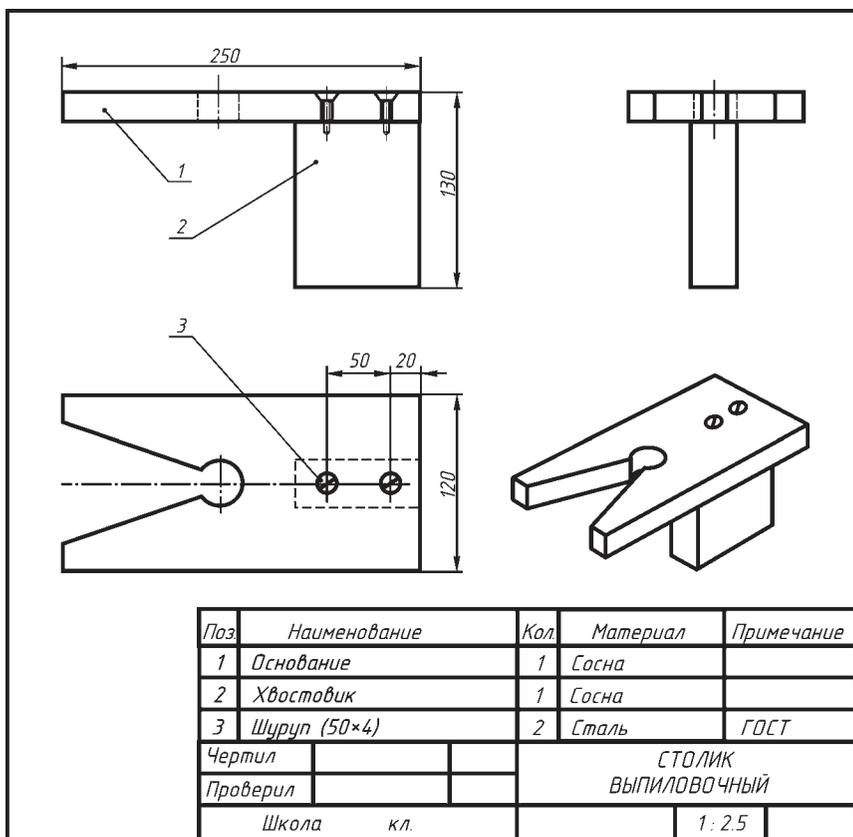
Сборочный чертёж и технический рисунок столика выпилочного
